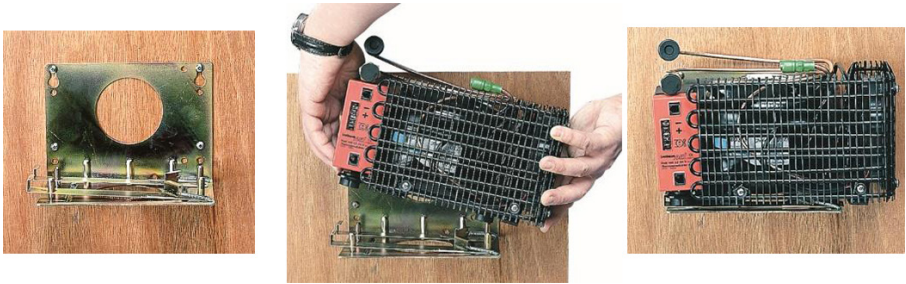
Detailansicht Anschluss Kompressorgruppe - Bügel
